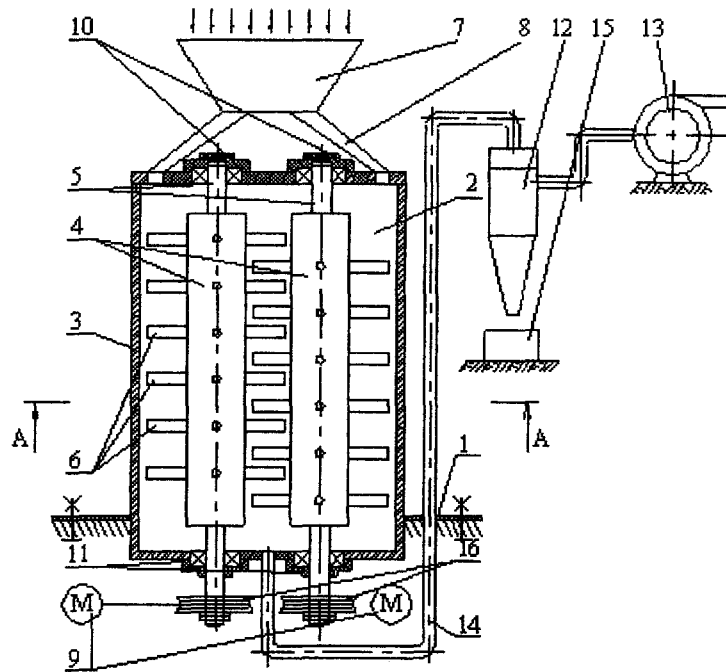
Схема мельницы ударного импульса: 1- станина; 2 - камера измельчения; 3 - корпус; 4 - цилиндрический ротор; 5 - ось; 6 - стержень-бил; 7 - загрузочное устройство; 8 - отвод; 9 - привод; 10 - верхняя опора качения; 11 - нижняя опора качения; 12 - классифицирующий циклон; 13 - вентилятор-компрессор; 14 - трубопровод; 15 - тара
